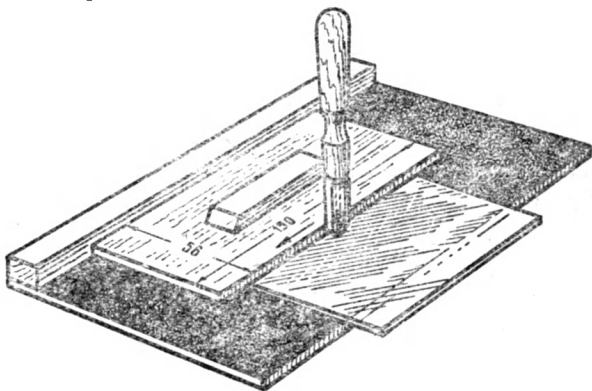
Приспособление для резания диапозитивных пластинок 13×18 см на три полоски.
